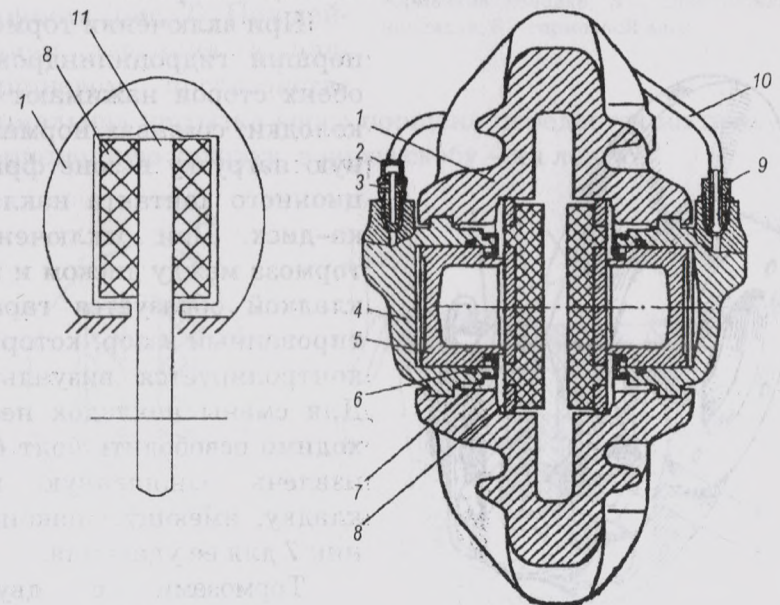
Дисково-колодочный тормоз автомобиля ВАЗ-2101 с неподвижной скобой: 1 – корпус суппорта; 2 – грязезащитный колпачок клапана выпуска воздуха; 3 – клапан выпуска воздуха; 4 – колесный цилиндр; 5 – поршень; 6 – уплотнительное кольцо; 7 – пылезащитный колпачок; 8 – тормозная колодка; 9 – штуцер трубки; 10 – трубка; 11 – тормозной диск
